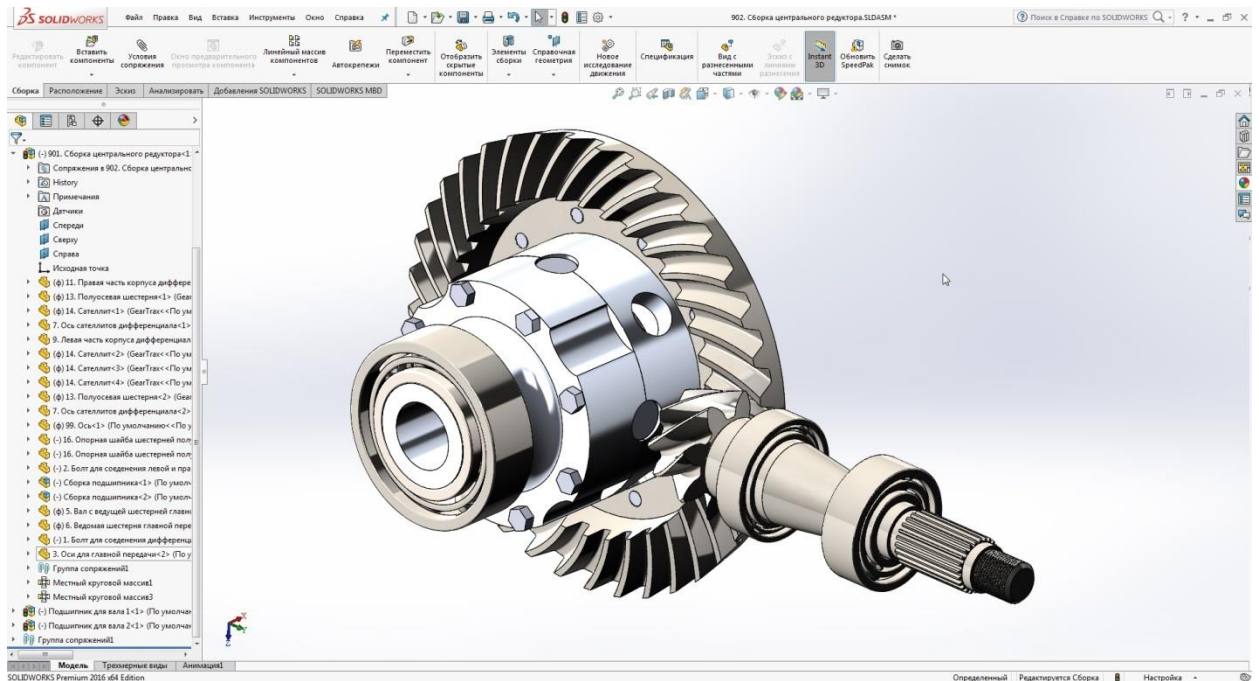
3D модель сборки центрального редуктора
